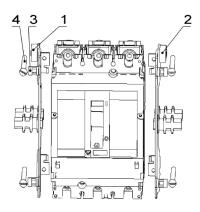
Детали для выключателя выдвижного исполнения.
